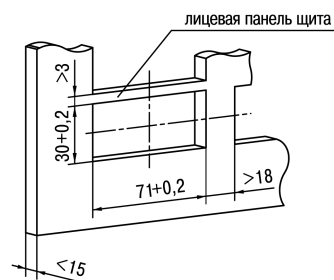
Габаритные размеры корпуса ЩЗ
